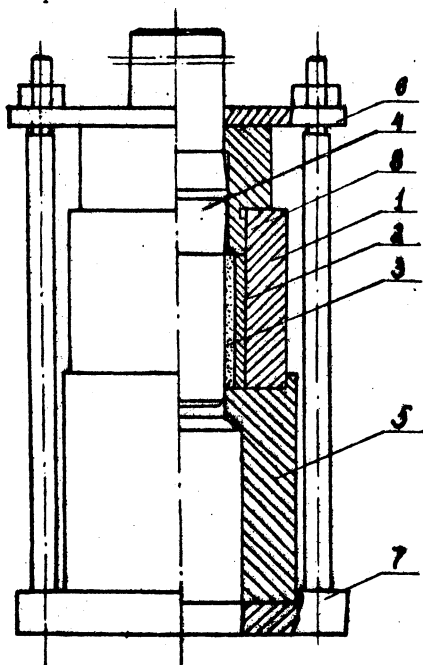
Рис. I. Схема лабораторной пресс-формы для нанесения порошкового слоя на внутреннюю поверхность трубчатой заготовки
